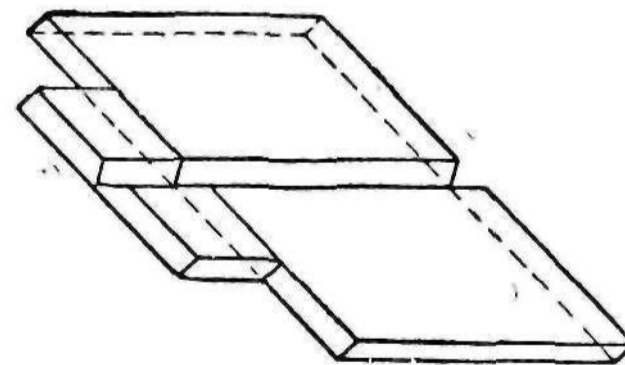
Вывод стыкового шва за пределы рабочего сечения (выступ по окончании сварки срубается)
